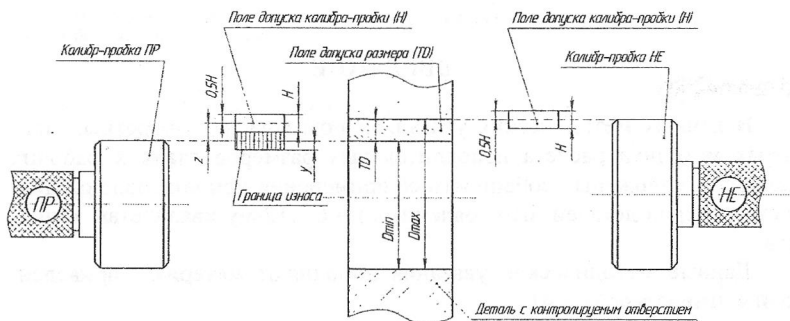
Схема расположения полей допусков калибров-пробок для контроля отверстий $D < 180$ мм, изготовленных по 6,7 и 8-му квалитетам точности: D_{\max} – наибольший предельный размер отверстия, мм; D_{\min} – наименьший предельный размер отверстия, мм; TD – допуск размера отверстия, мкм; H – допуск на изготовление калибра-пробки, мкм; Z – координата середины поля допуска на изготовление проходного калибра-пробки, мкм; Y – допустимый выход размера изношенного проходного калибра-пробки за границу поля допуска размера, мкм.
